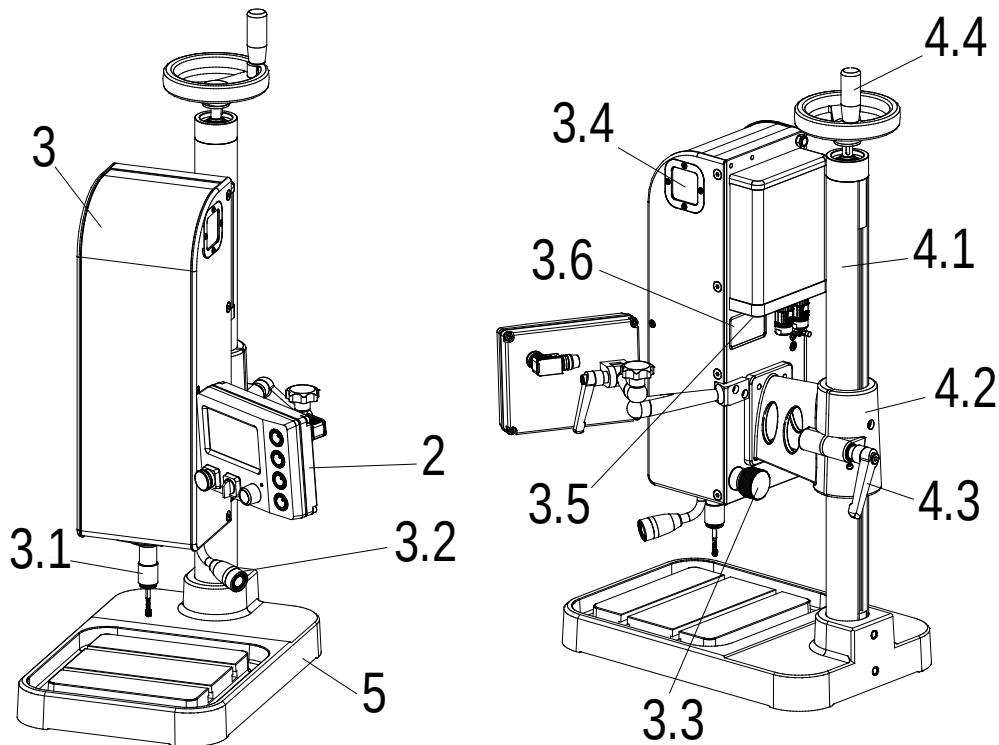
Vue avant et arrière de la machine à fileter avec unité de commande
